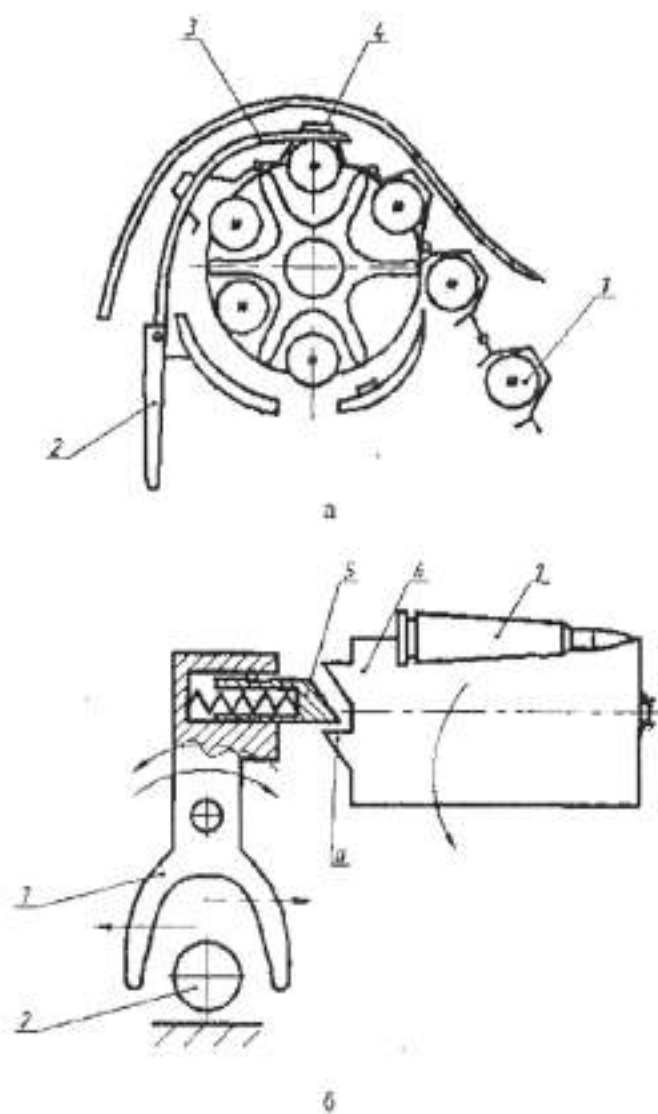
Схема патрно-подающего механизма: а – при перемещении ленты; б – при перемещении барабана:
